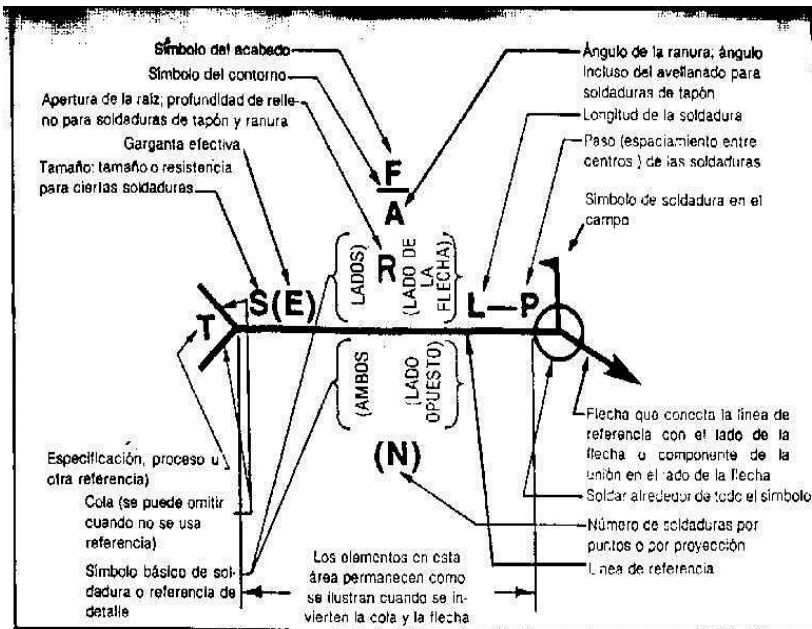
Símbolos estándar para soldadura
